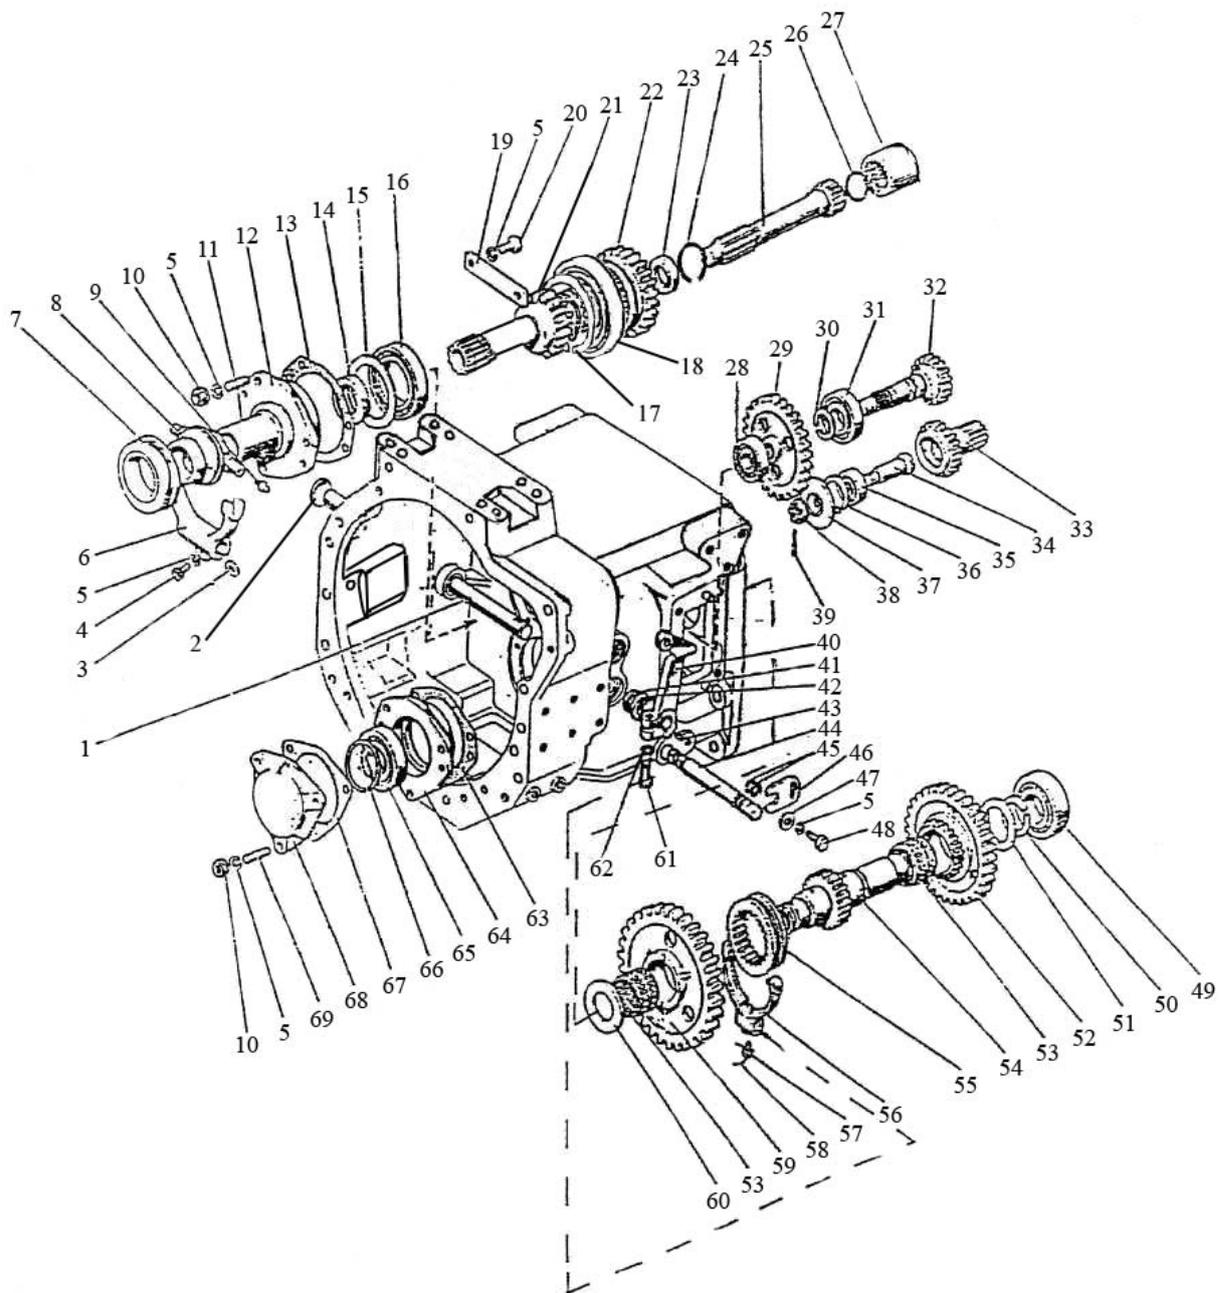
Корпус сцепления (2022.4-1600010-01) (с КП 24x12)
